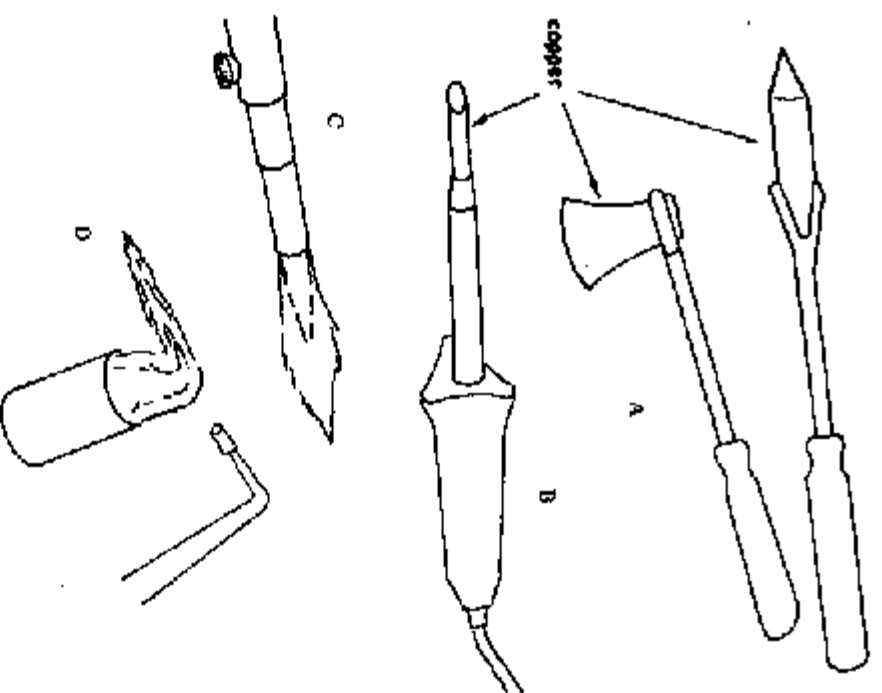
La soldadura puede aplicarse con un cautín de cobre: (A,B) o con un soplete de flama abierta: (C,D).
